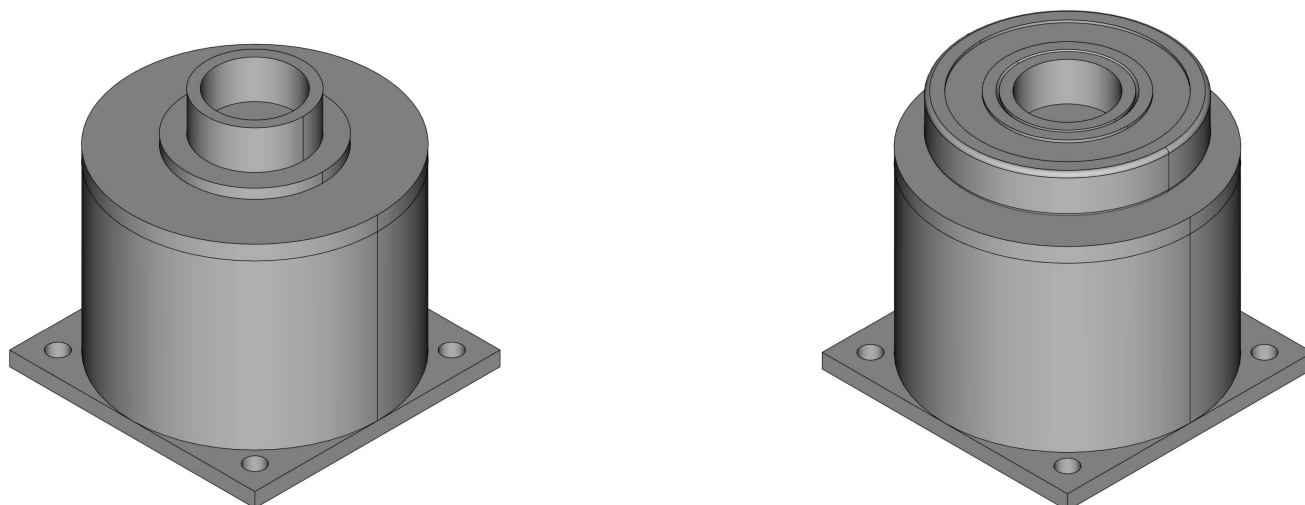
“Base rotatoria, detalle parte inferior; Izquierda, base sin rodamiento; Derecha, rodamiento montado”.
